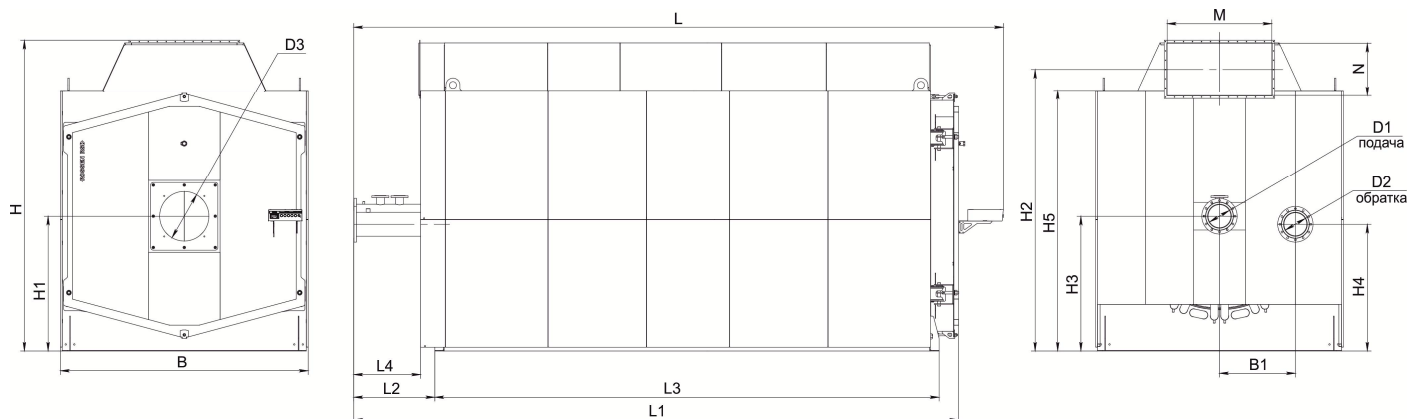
Габаритные и присоединительные размеры котлов RS-D12000, RS-D15000
